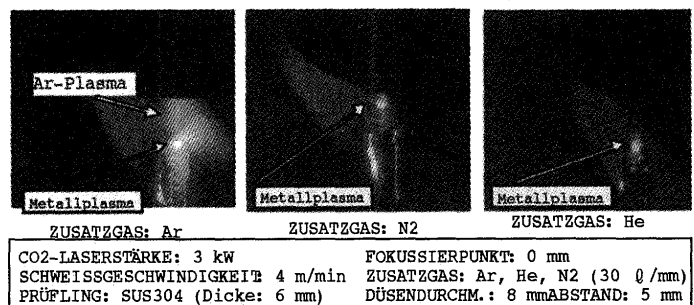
Typische Videobilder der Laserschweißung an SUS304
